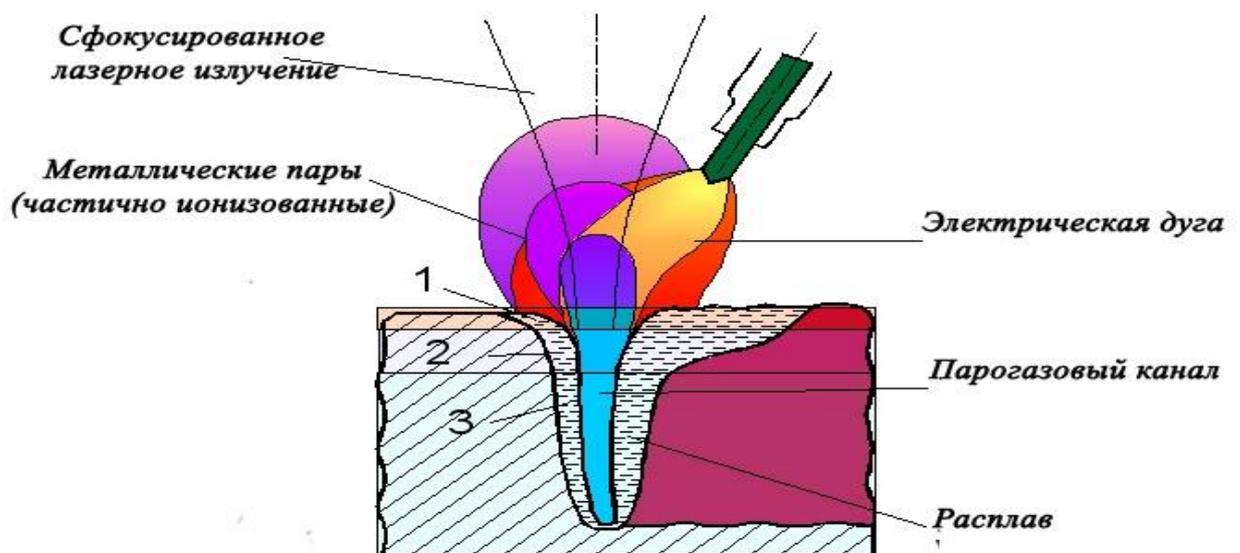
Гибридная лазерно-дуговая сварка
